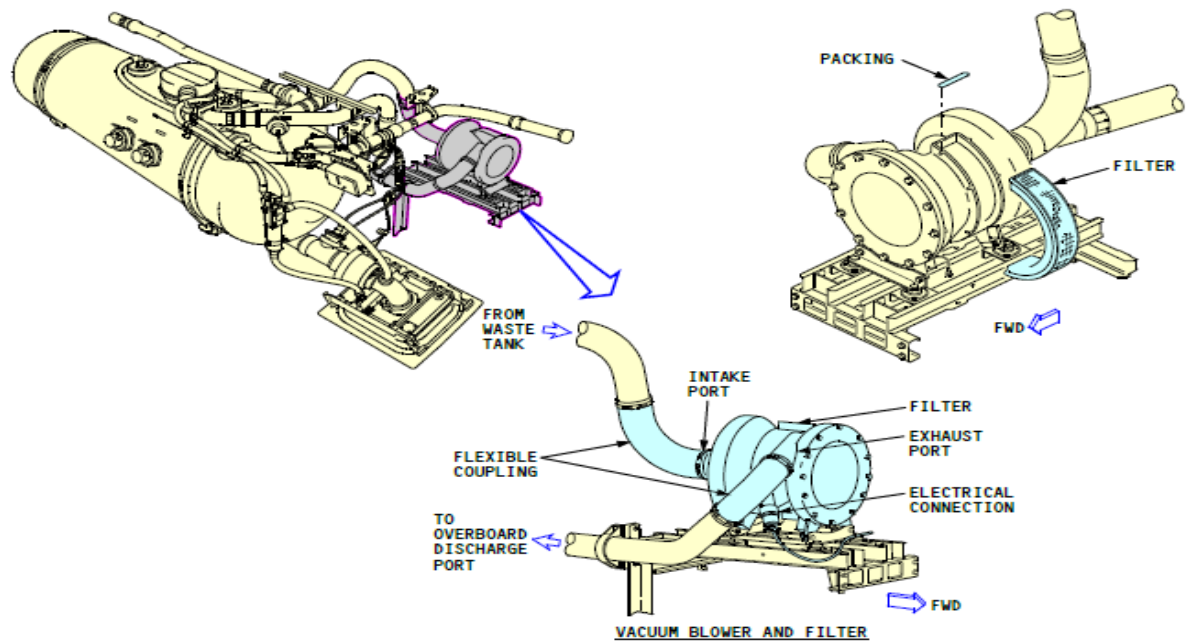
Toilet Assembly Boeing 737-900 ER [3]
